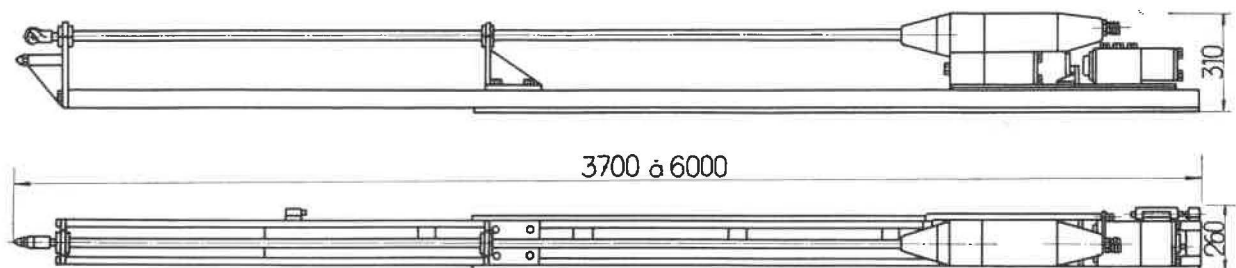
Vue de profil ou coupe horizontale de la foreuse roto-percutante type « Kombi P II/4 ».
